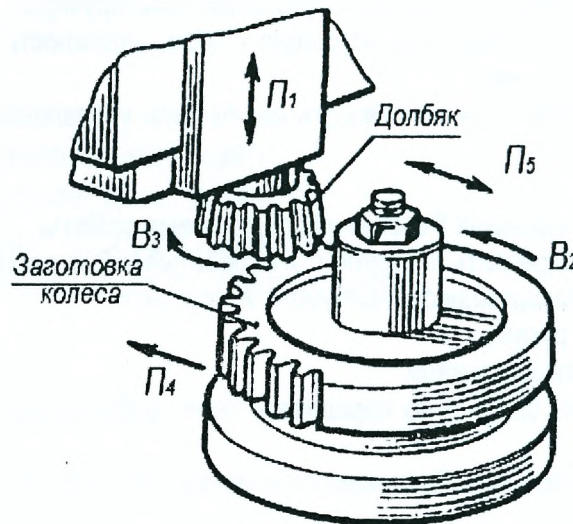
Схема нарезания цилиндрического зубчатого колеса долбяком
